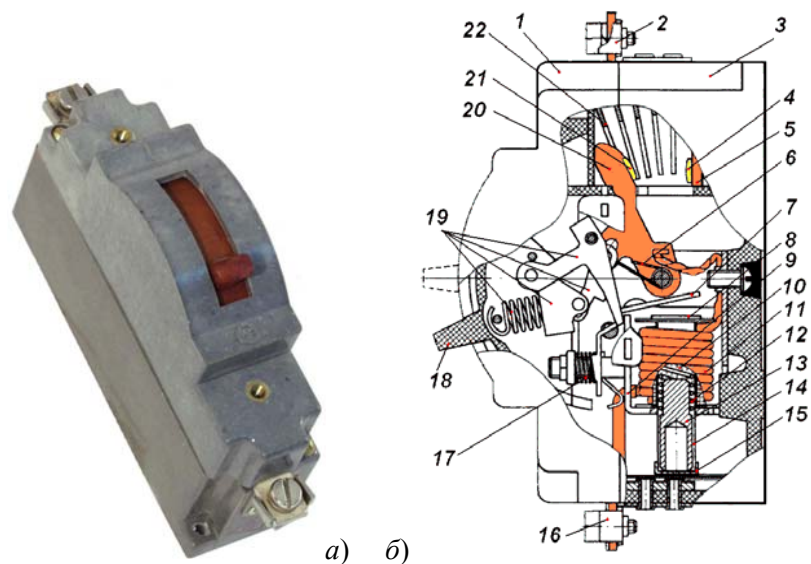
Общий вид (а) и конструкция автоматического выключателя А63 (б):
